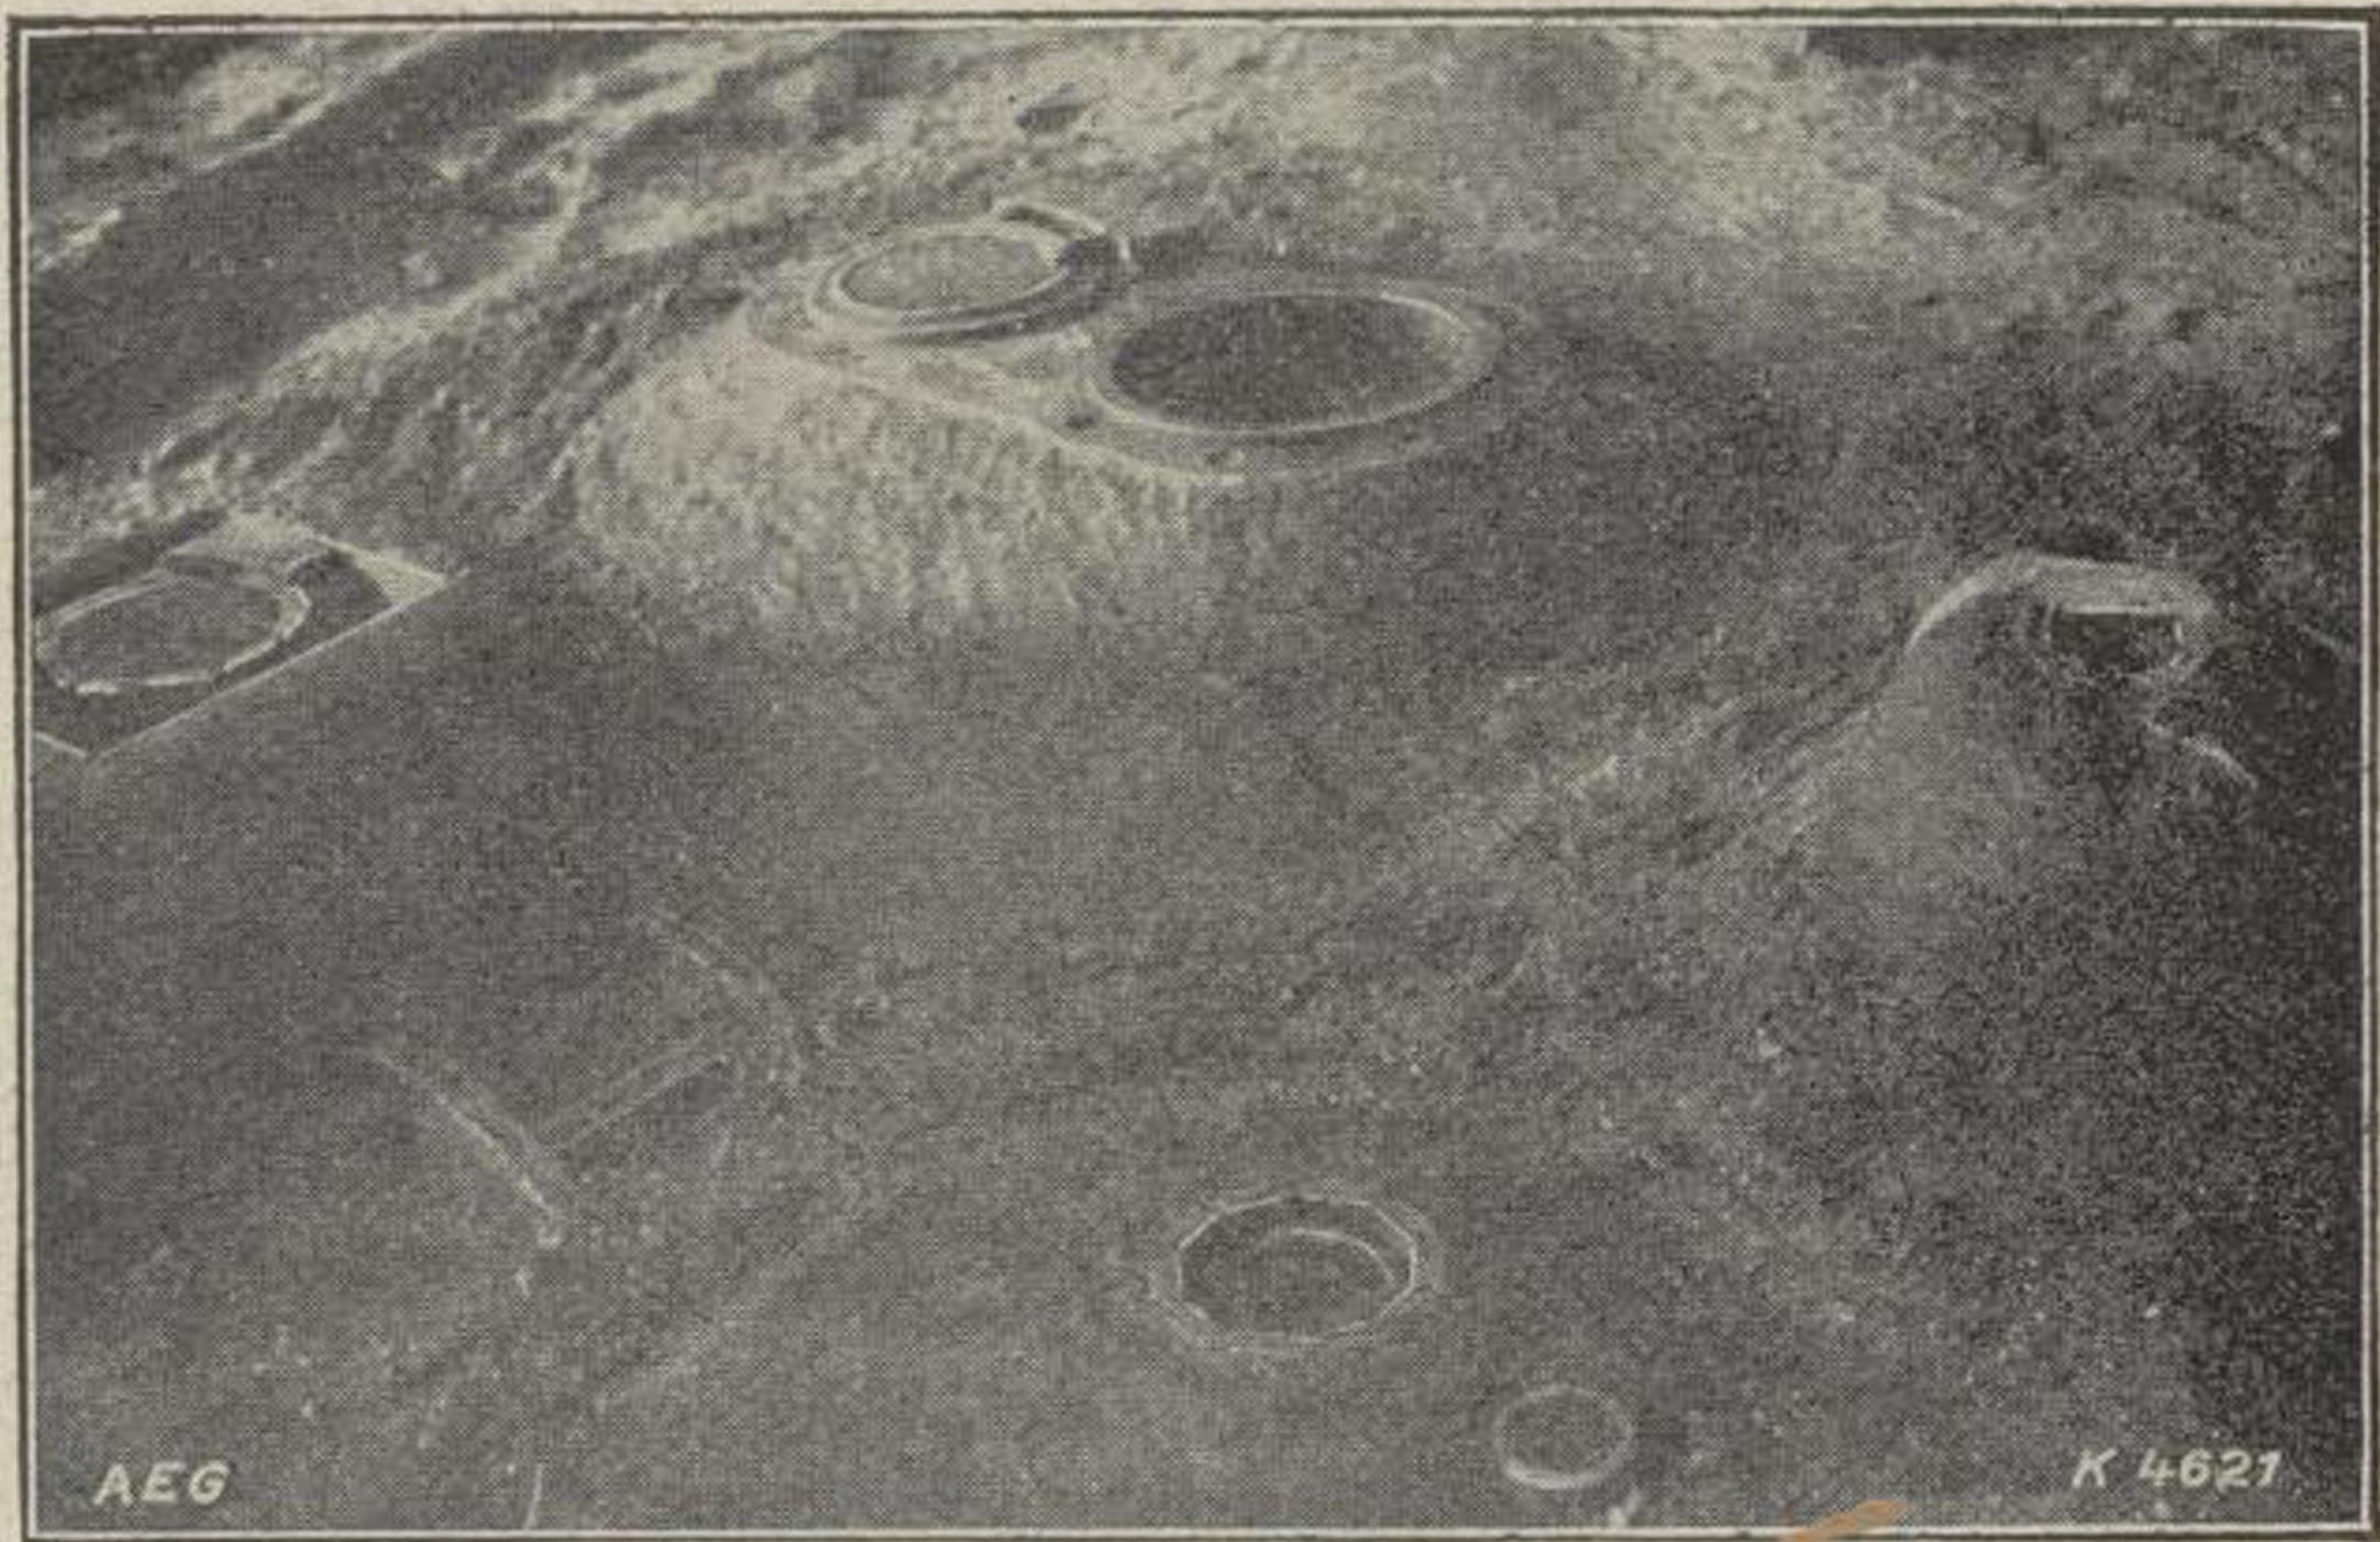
Pequeñas piezas de hierro fundido, moldeadas en arena para la soldadura en caliente.
